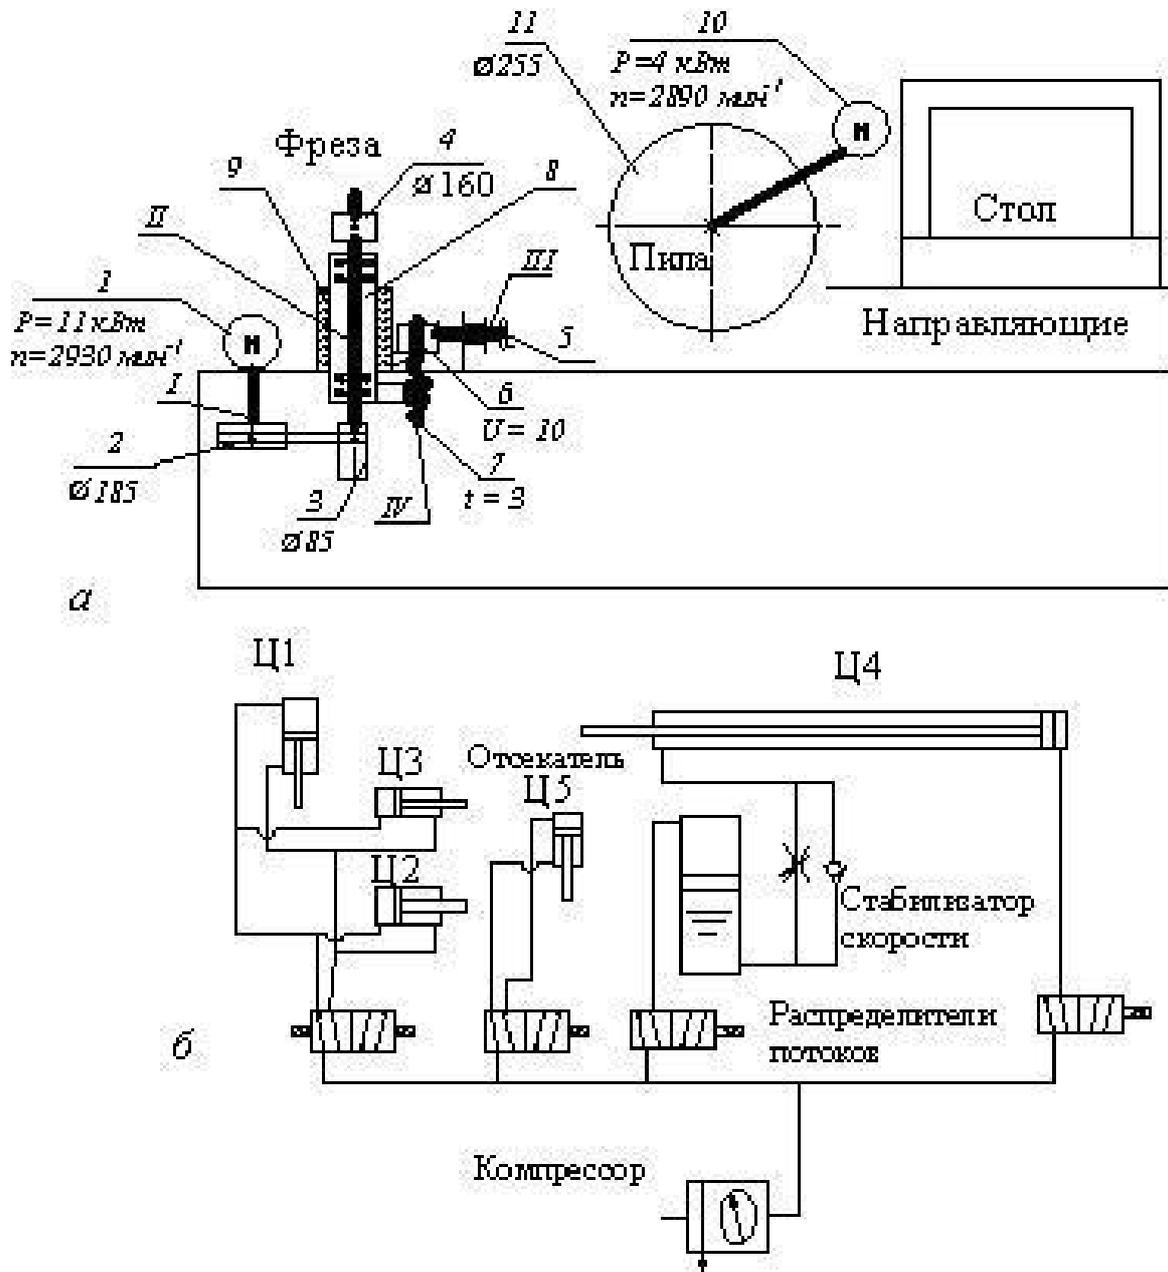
Гидрокинематическая схема шипорезного станка TSK 15P:
